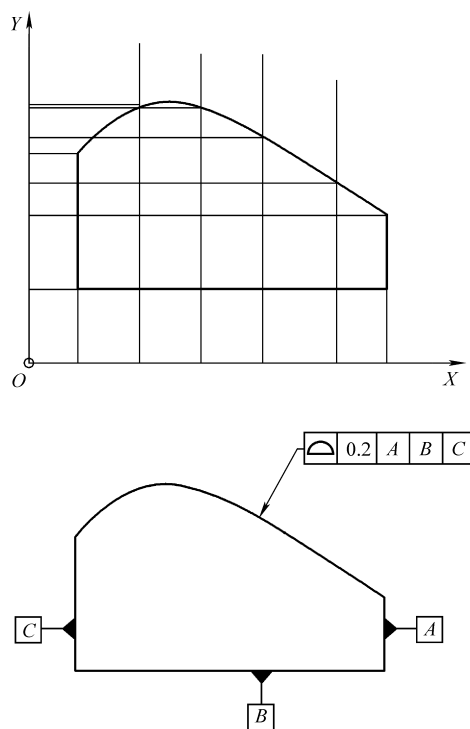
尺寸公差和几何公差对于异形特征的定义
